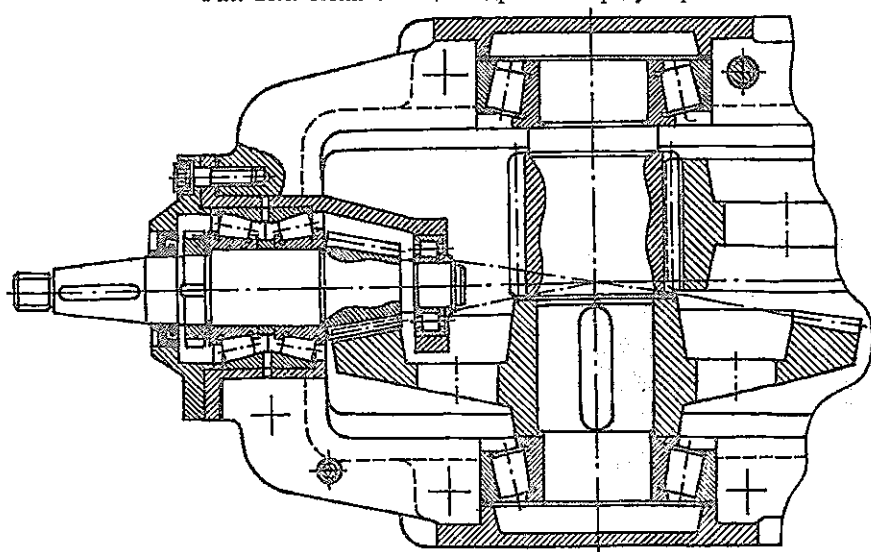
Быстроходная ступень коническо-цилиндрического редуктора
